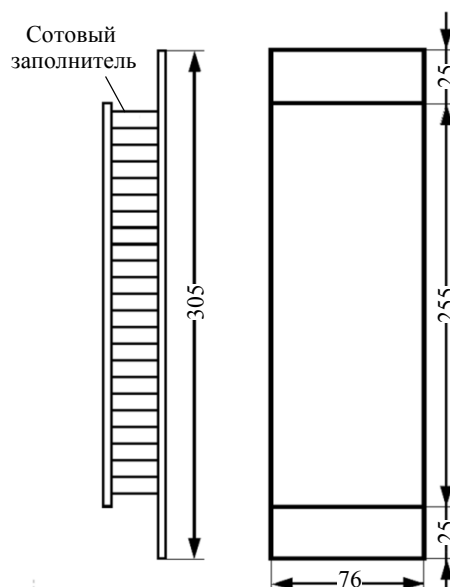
Эскиз образца трехслойной сотовой панели для испытания на отслаивание обшивки
